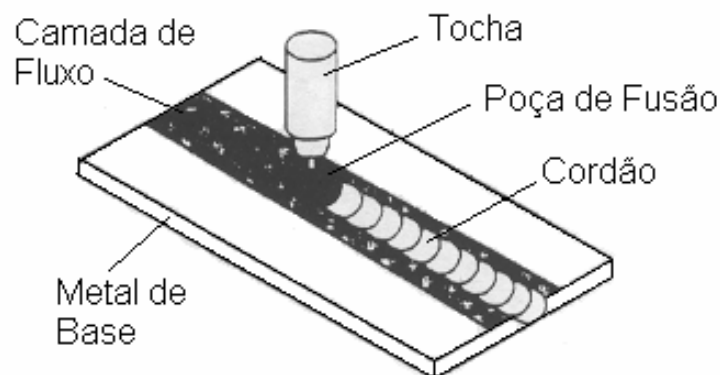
Soldagem ATIG (LUCAS & HOWSE, 1996).
